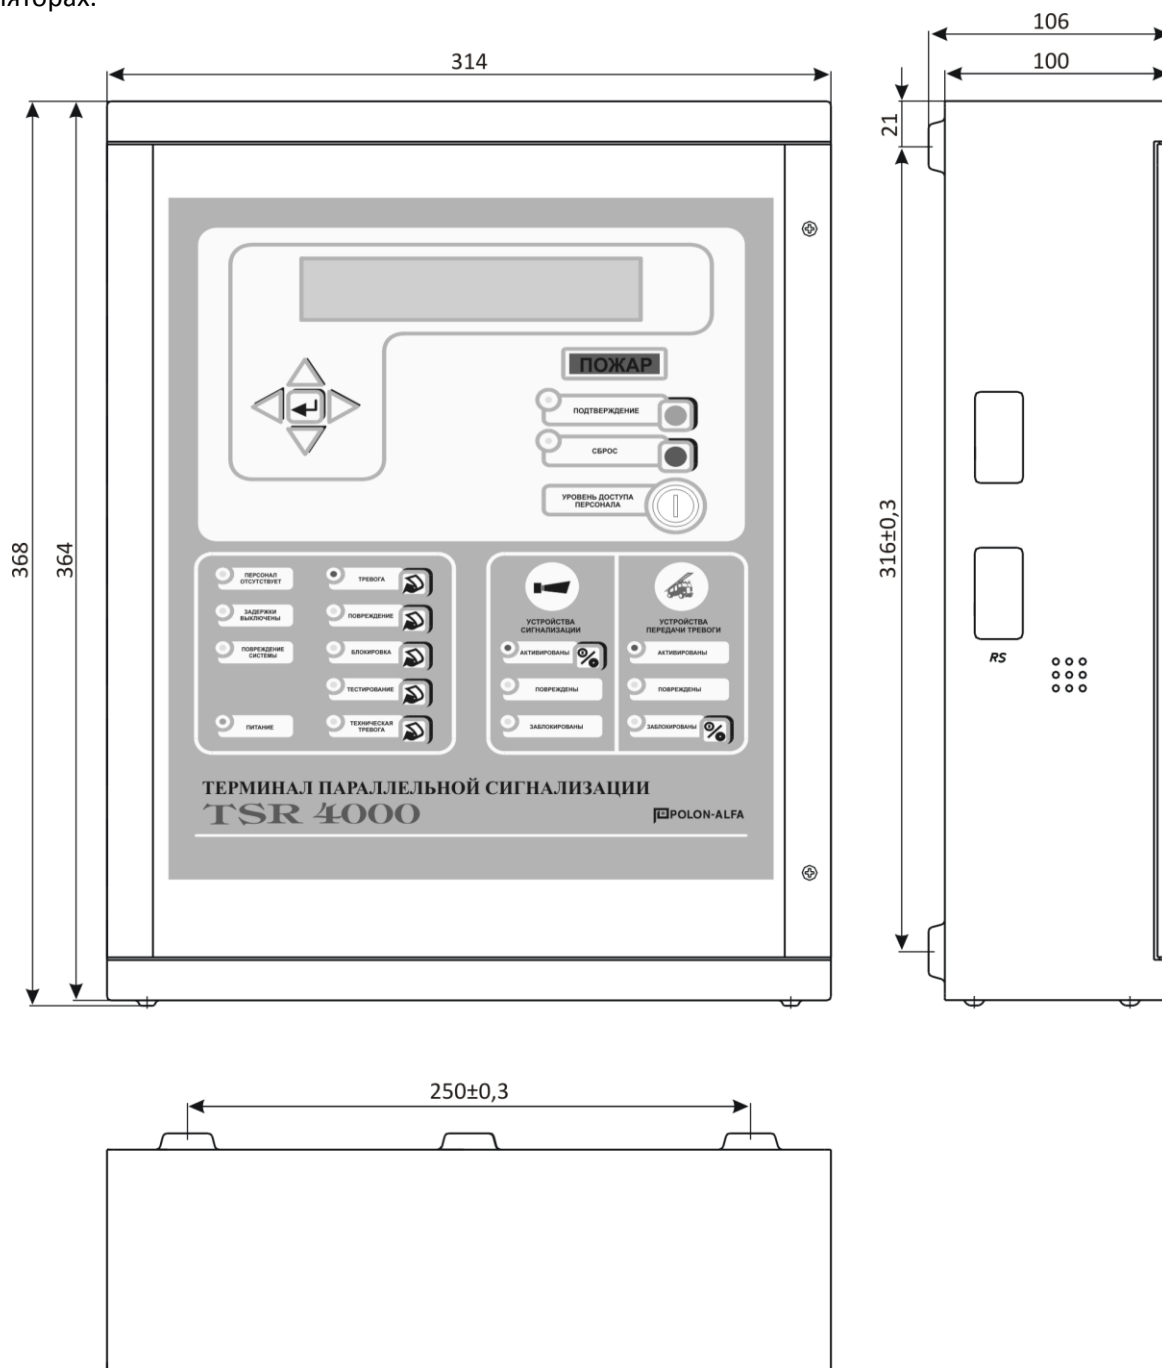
Внешний вид и основные размеры терминала TSR-4000
